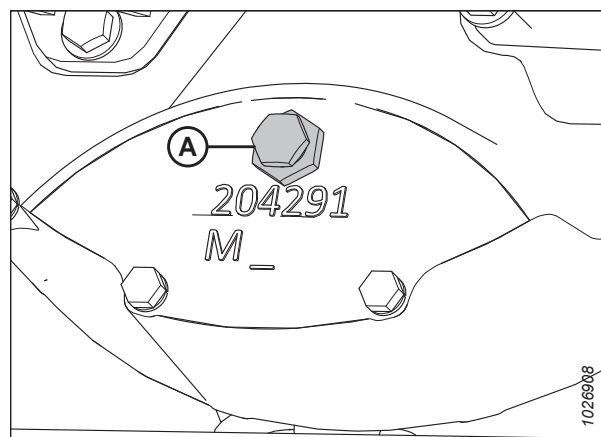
Пробка отверстия для контроля масла редуктора
